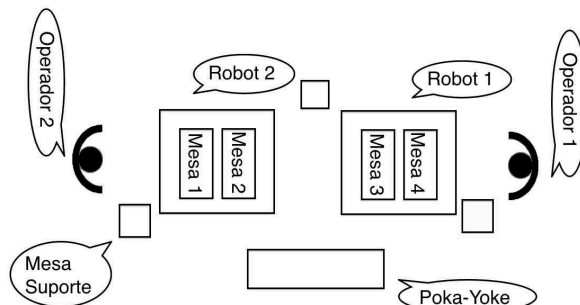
Ilustração da disposição das operações na Célula de Soldadura
